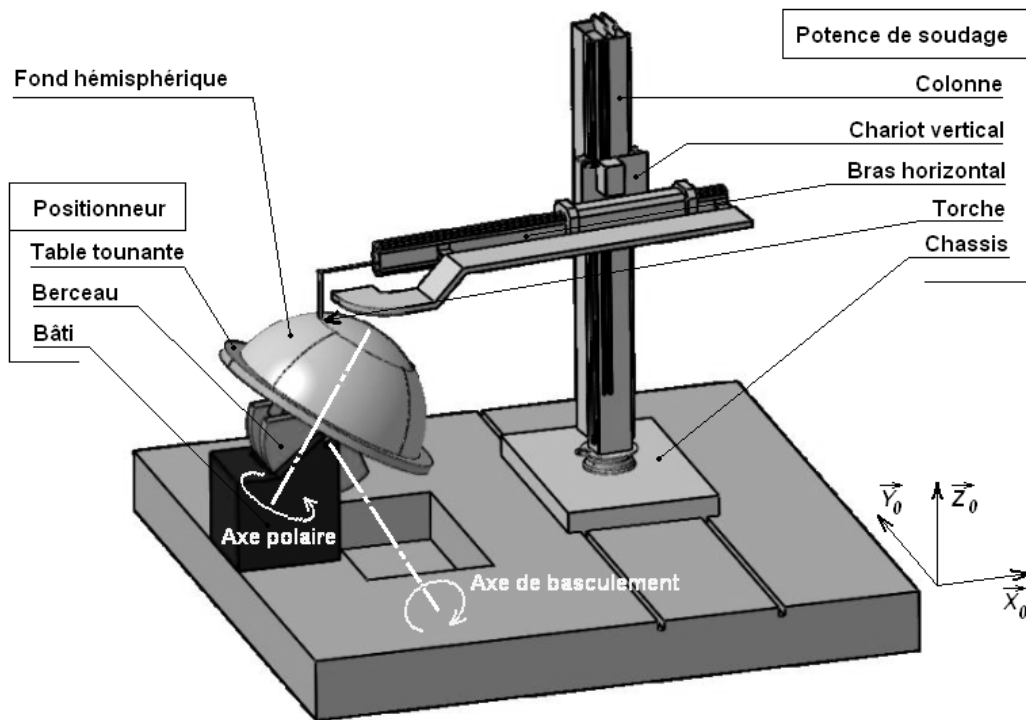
Vue générale de la machine de soudage automatisée
